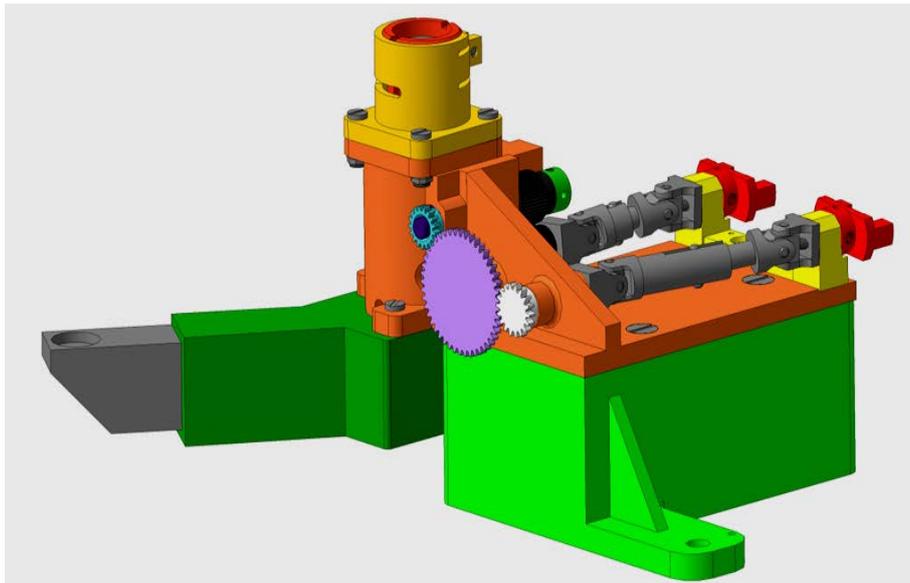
3D-прототип под сборки механизма визира мехатронного прибора
